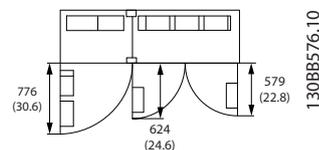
Пространство перед корпусом IP21/IP54, типоразмер F12
